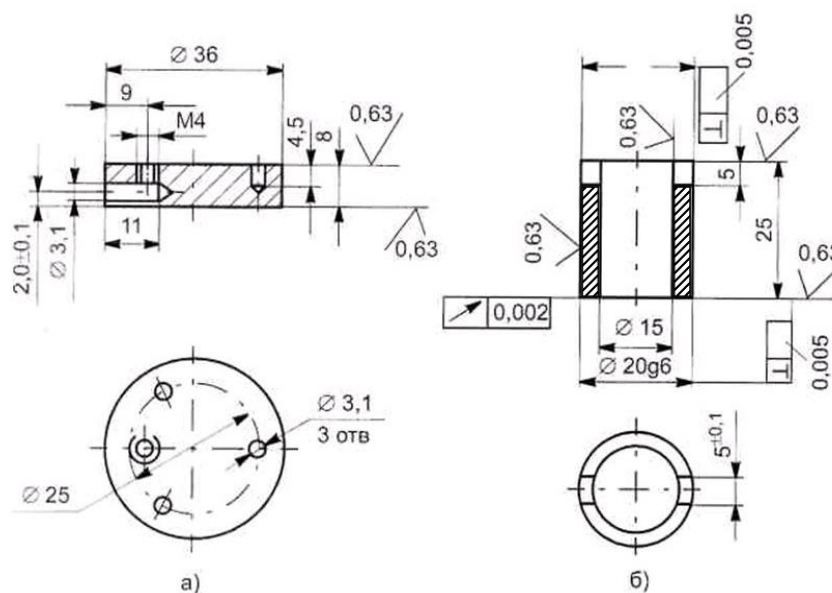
Конструкция образцов для стенда "шайба-диск": а - нижний образец (НО); б - верхний образец (ВО).
